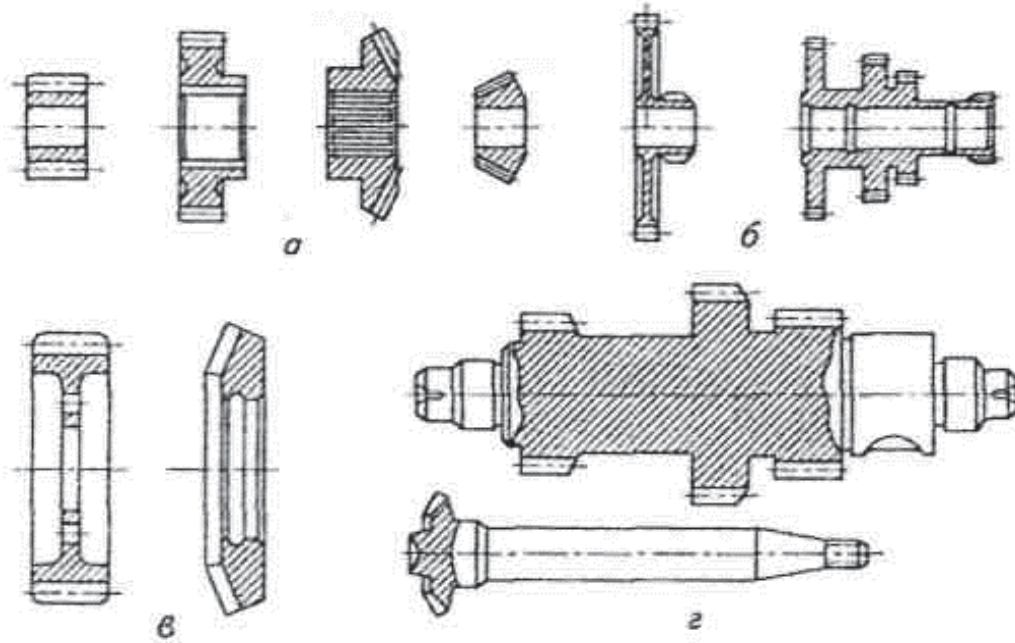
Основные группы цилиндрических и конических зубчатых колес:
